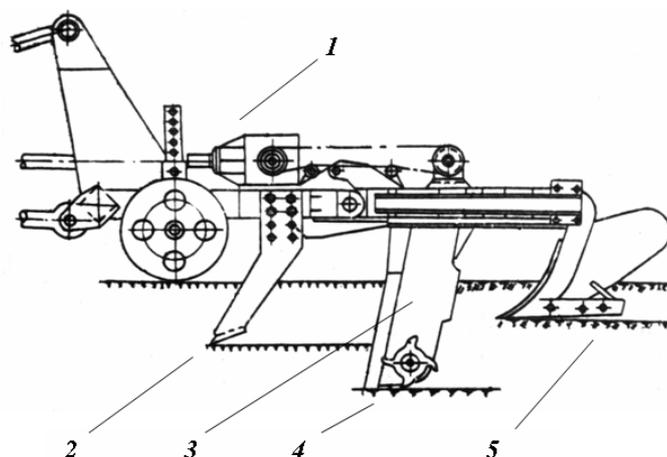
Устройство для почвенно-мелиоративной ротационной фрезерной обработки почвы ПМС-70, вид сбоку: 1 — механический привод; 2 — рыхлящий нож; 3 — редукторная стойка; 4 — ротационно-фрезерный рыхлитель иллювиального и подсолонцового горизонтов почвы; 5 — пассивный плужный корпус для обработки верхнего слоя почвы [6]
